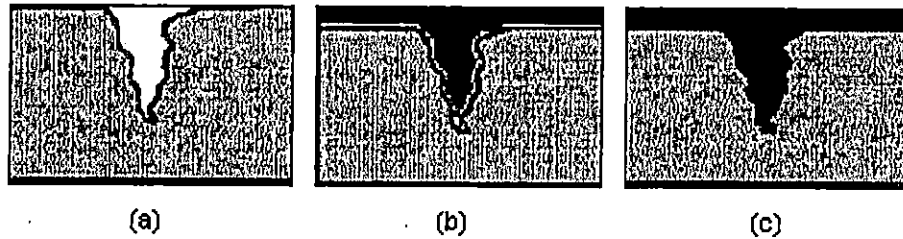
Aplicación de un líquido penetrante sobre una junta de soldadura, para detectar defectos no apreciables a simple vista ni a pruebas de VT. ⁽¹⁻³⁵⁾
